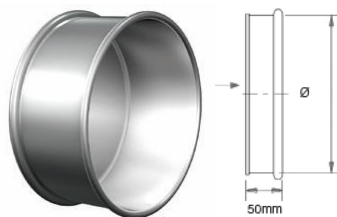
Tampa cega (QFS Oil Mist & Cutting Fluid)
